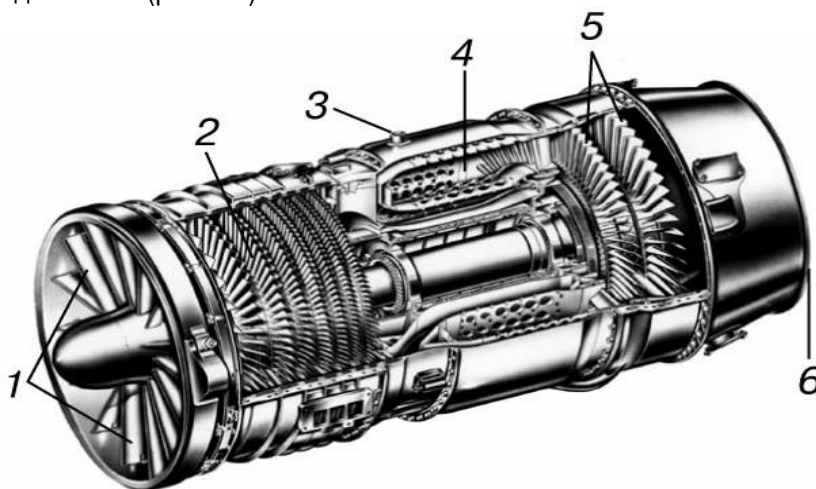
Турбореактивный двигатель с осевым компрессором: 1 – воздухозаборник; 2 – компрессор; 3 – подача топлива; 4 – камера сгорания; 5 – турбина; 6 – сопло.
